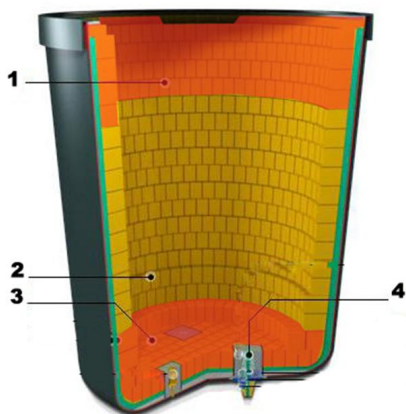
Схема расположения изнашиваемых зон сталеразливочного ковша: 1 – шлаковый пояс; 2 – стены; 3 – днище; 4 – гнездовой блок
